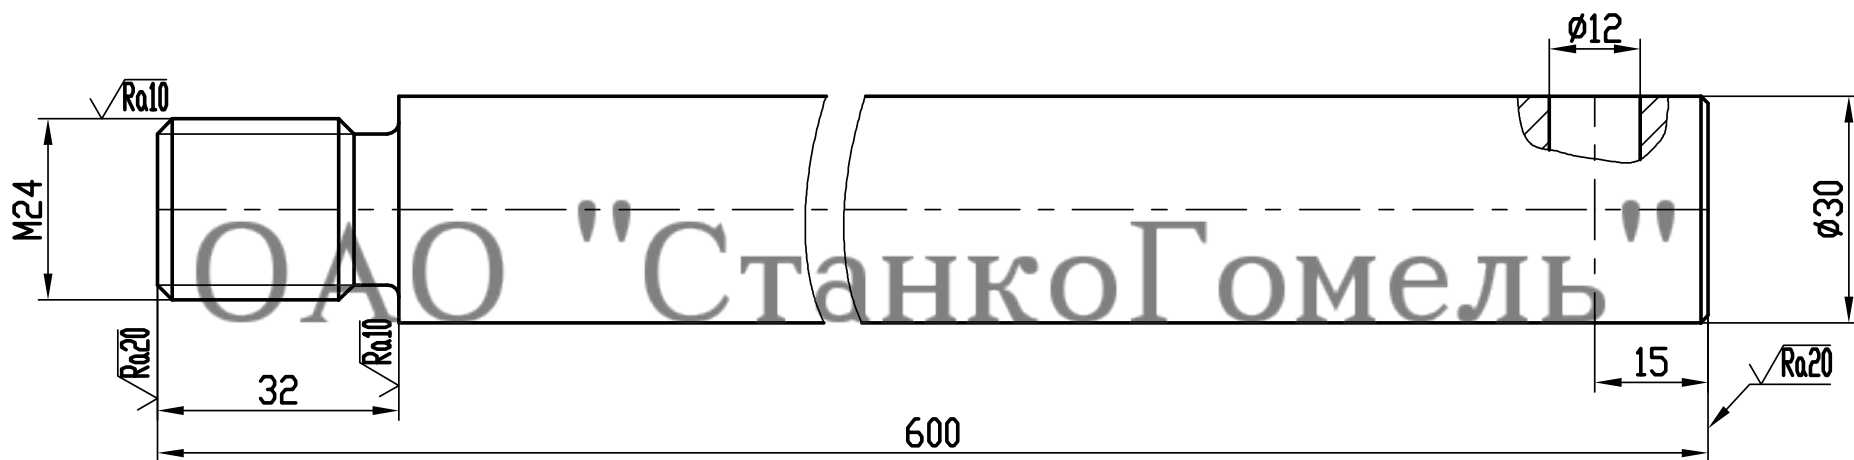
Приспособление для демонтажа коробки скоростей из стойки
